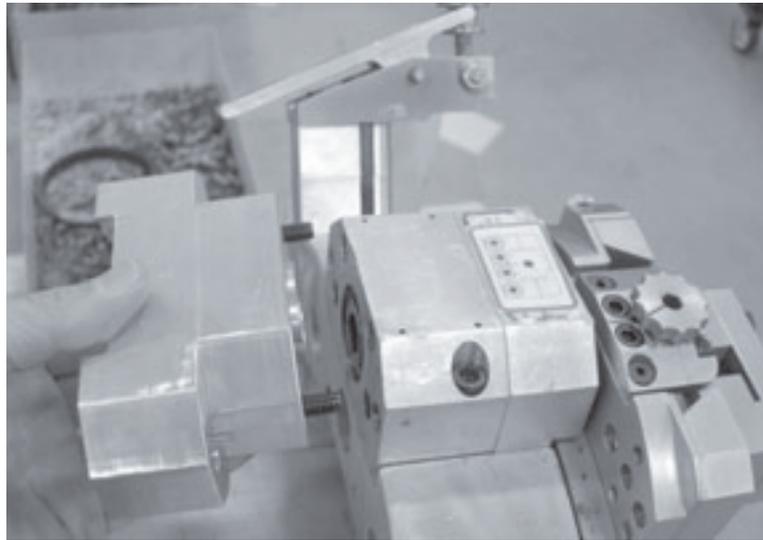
Collegare l'adattatore del motore idraulico alla sede pignone.
